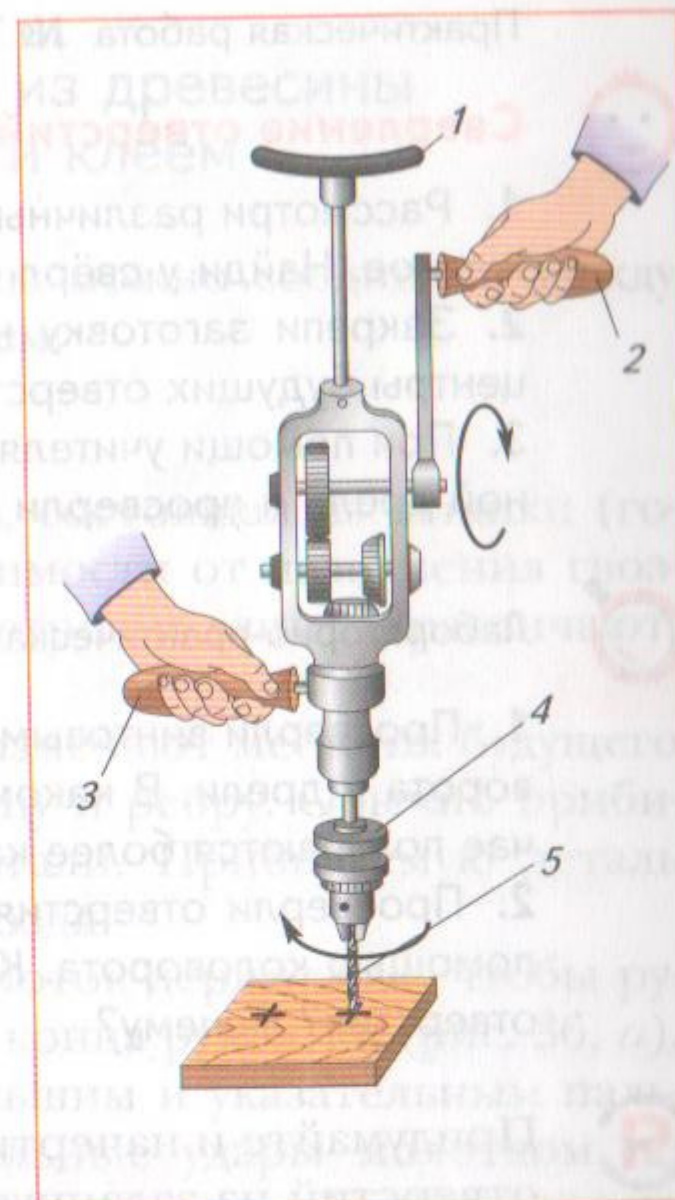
Устройство ручной дрели и приём сверления: 1 — корпус с упором; 2 — рукоятка вращения; 3 — рукоятка захвата; 4 — патрон; 5 — сверло
